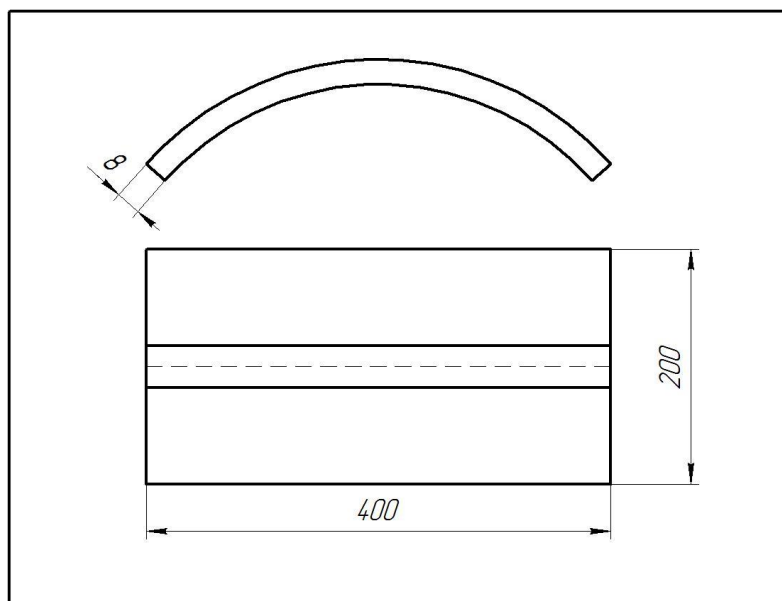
Образец из сегмента сварной трубы $\varnothing 530$.
